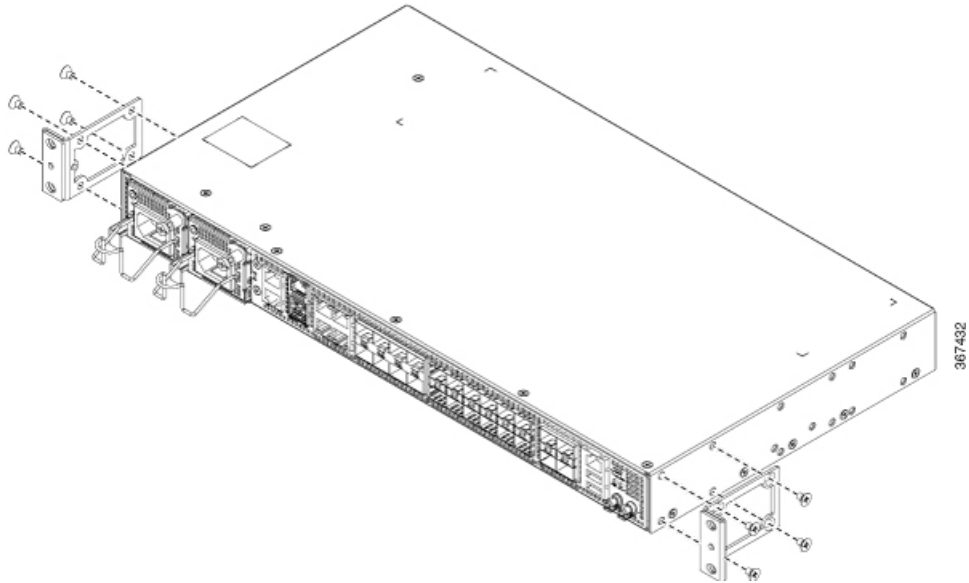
Fixar os suportes de montagem no router para rack EIA de 19 polegadas (posição intermédia)
